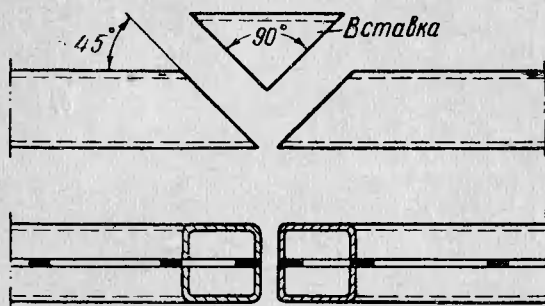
Подготовка концов двух шин коробчатого профиля для сварки между собой с помощью вставки при монтаже на горизонтальном участке трассы. На боковых и верхней сторонах шин необходимо подготовить (разделить) кромки для аргонодуговой сварки. Нижний шов заваривается угольным электродом.
